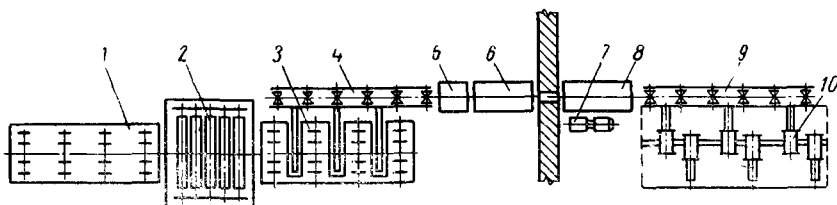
Схема непрерывной поточной линии химической очистки струйным способом
